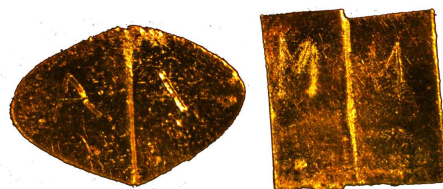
Soldadura autógena. La zona de soldadura resultante es lisa y se distingue solamente por una pequeña depresión entre las dos láminas.
